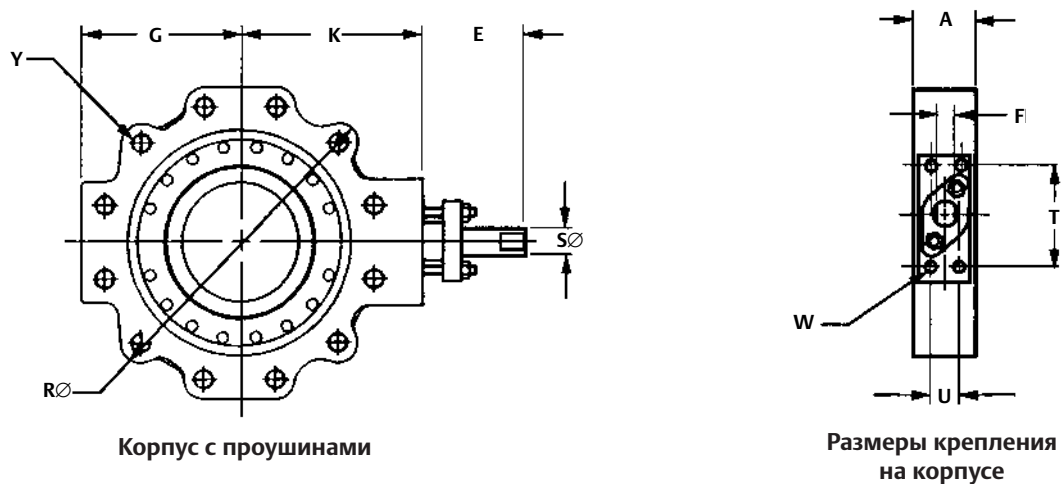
Размеры затвора 8560 с валом с двумя лысками
